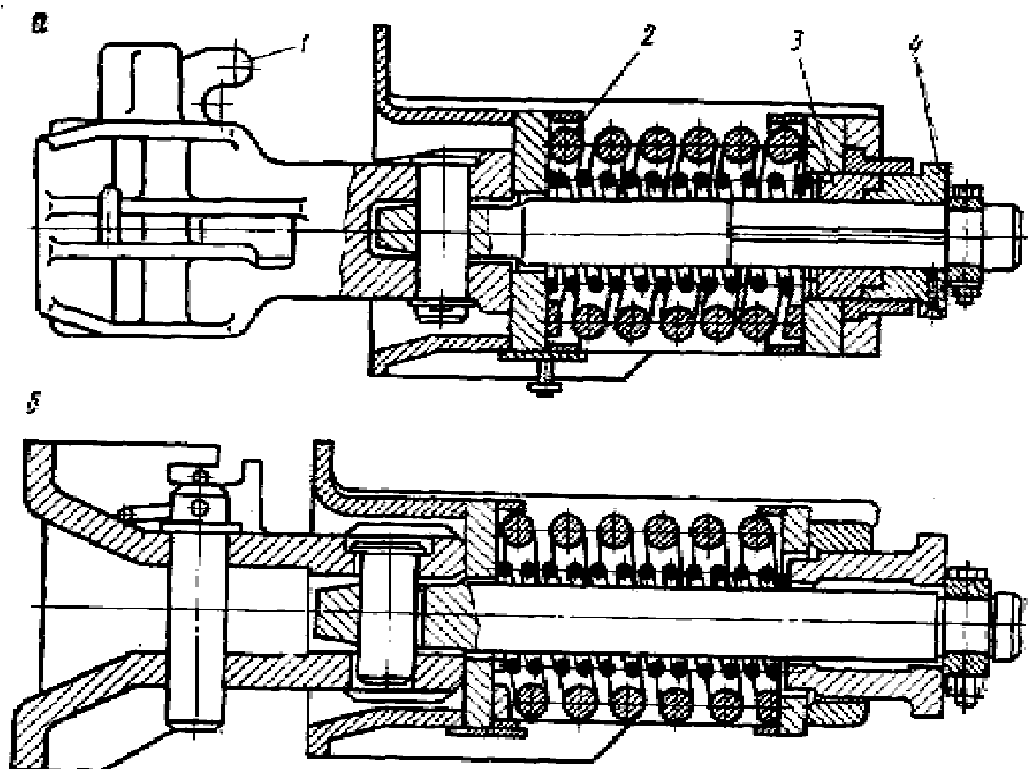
Сцепки вагонеток: а — автоматическая вращающаяся; б — звеньевая вращающаяся
